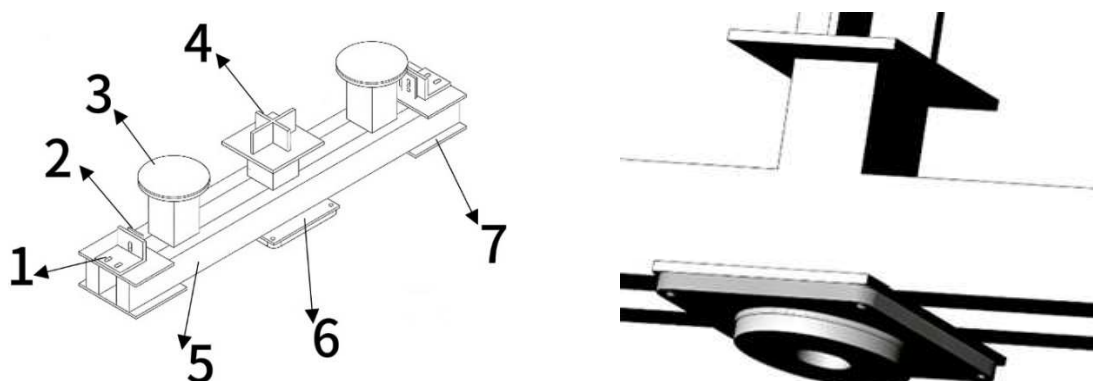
Транспортное устройство для транспортировки вагонов метрополитена
